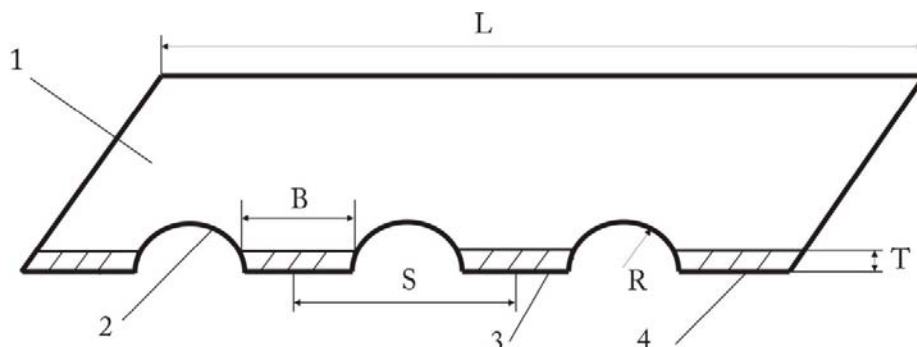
Схема наплавки зубьев ножа твердосплавным порошком: 1 – нож; 2 – вырезы; 3 – зубья; 4 – зона наплавки.
